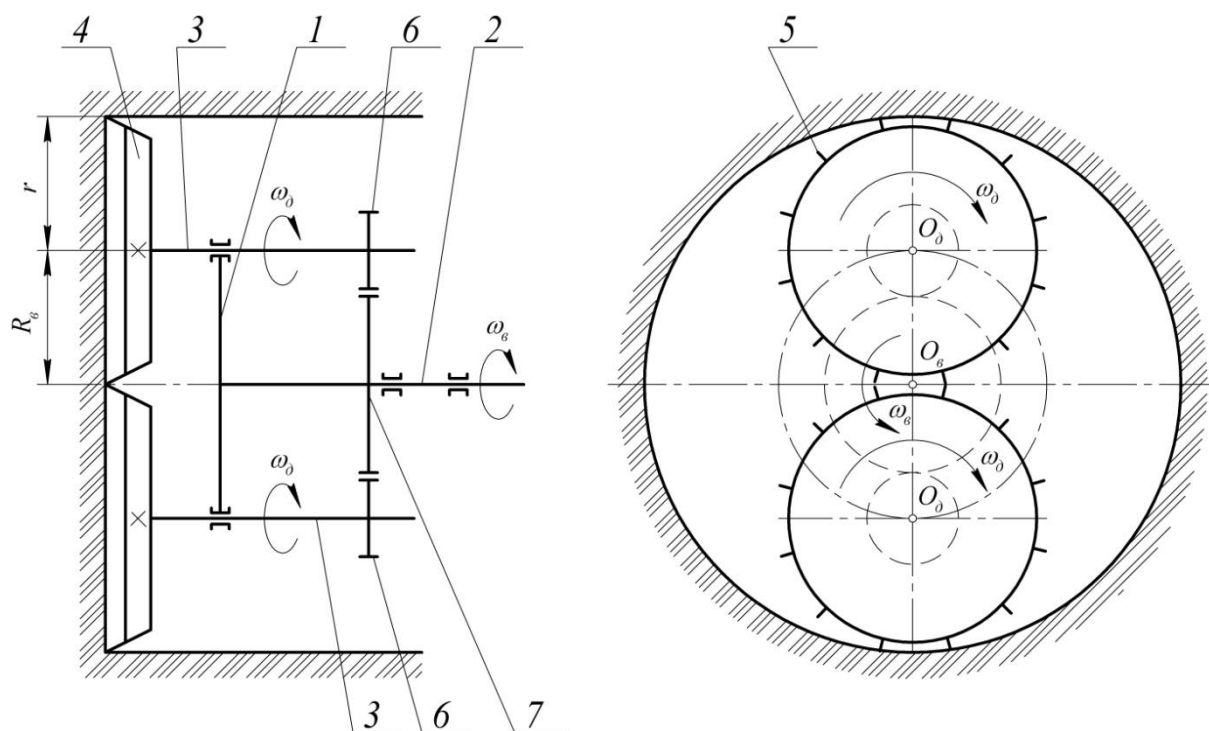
Схема плоско-планетарного зубурювальника: 1 – водило; 2 – головний вал; 3 – вали дисків; 4 – робочі диски; 5 – різальний інструмент; 6 – сателіти; 7 – сонячне колесо
